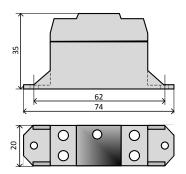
Габаритные размеры устройства для монтажа на поверхность
